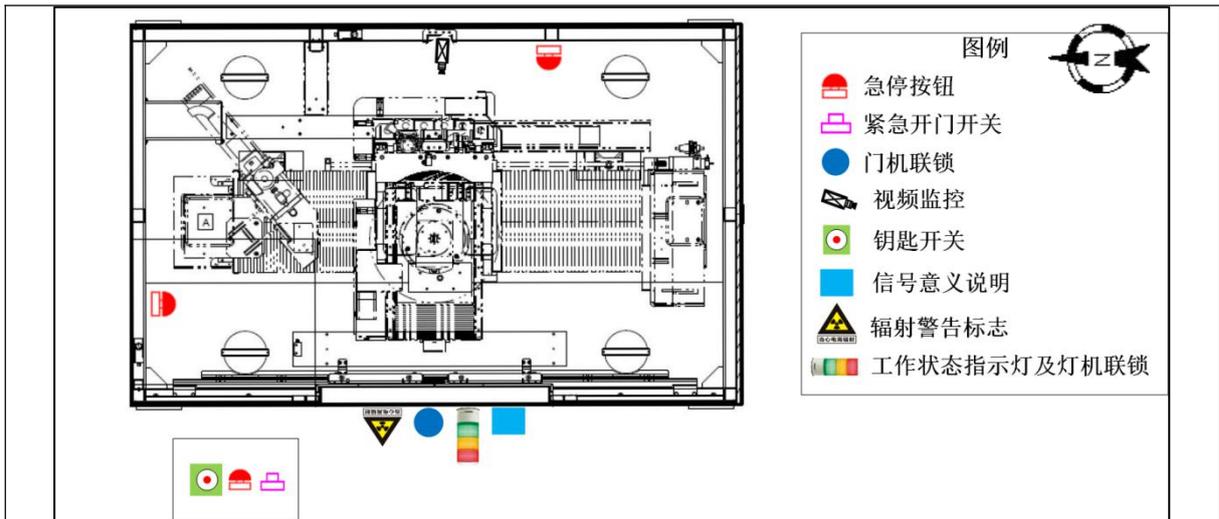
本项目 6#工业 CT 装置辐射防护与安全措施布置图
